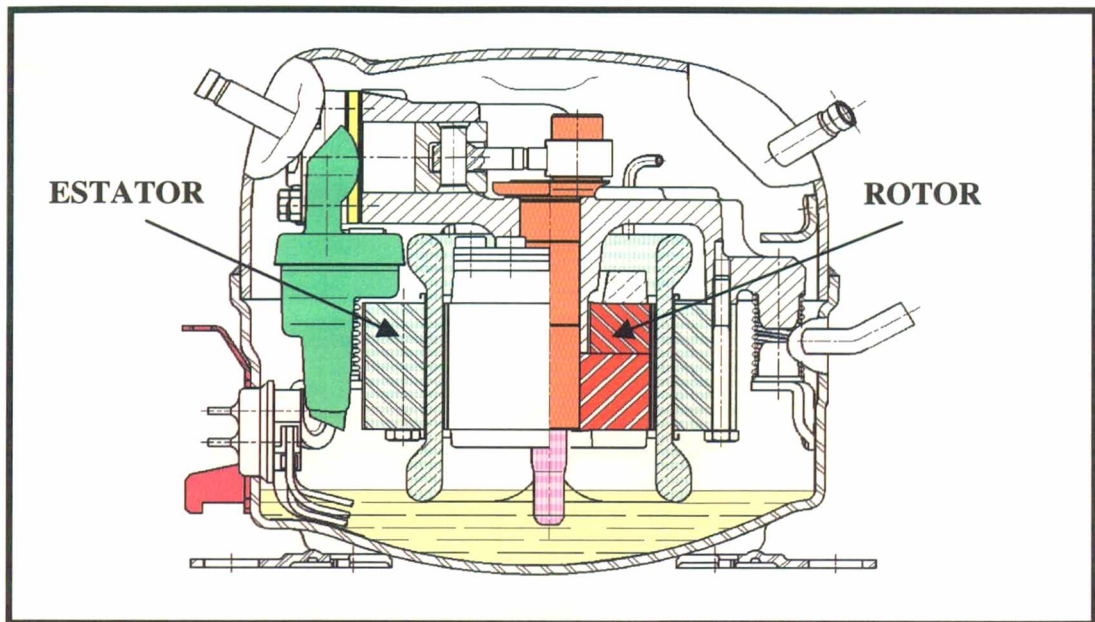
Desenho de conjunto de um compressor de refrigeração.
